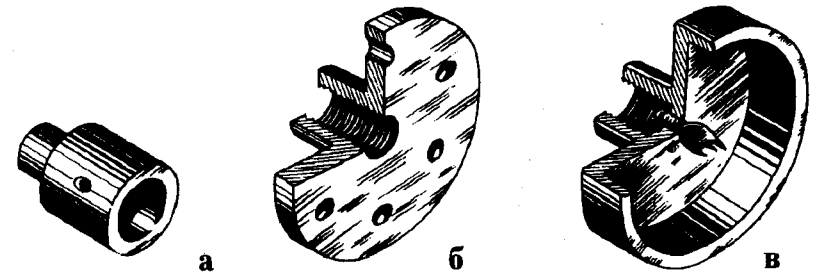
Шпиндельные приспособления для крепления заготовок при точении: а — патрон; б — планшайба; в — трезубец
